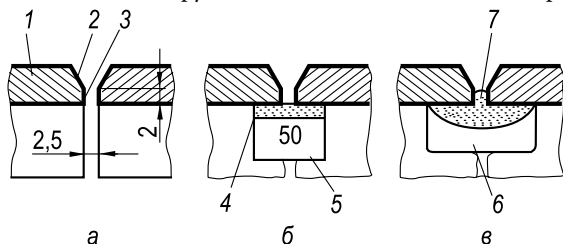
Типы сварных соединений: а — сварной V-образный стык; б — сварной стык с цилиндрическим подкладным кольцом; в — сварной стык с фасонным подкладным кольцом
